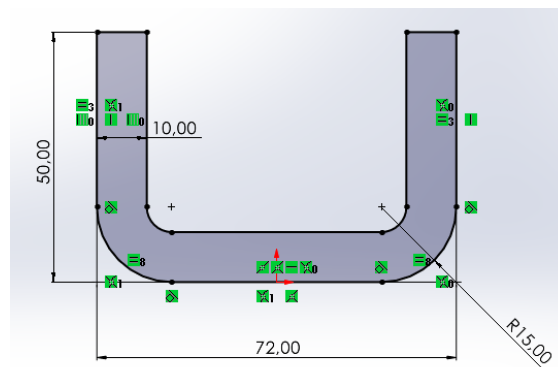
Croquis horquillas de la junta cardán en SolidWorks.
